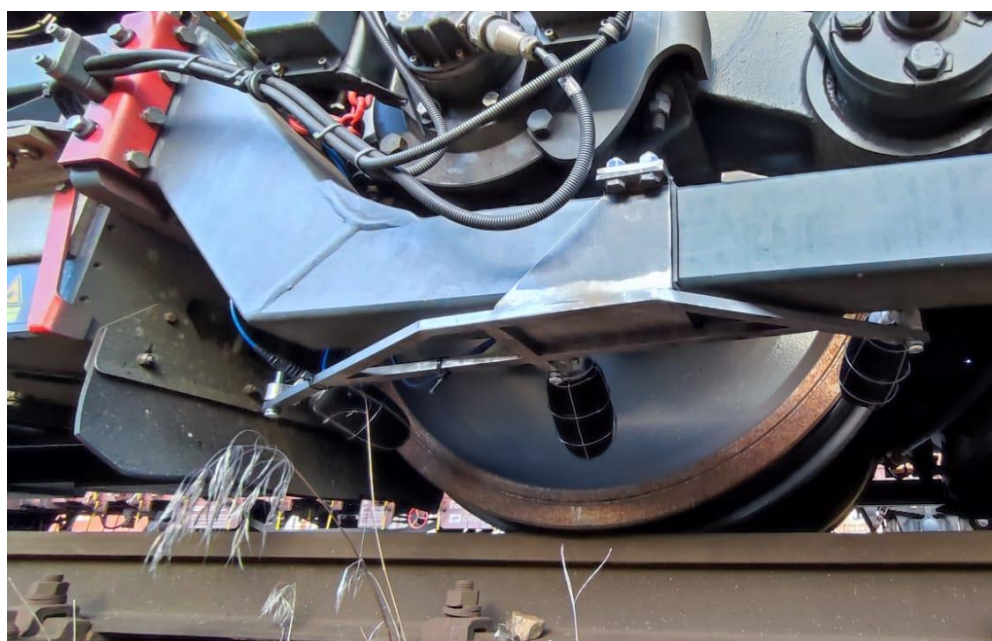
Prototypování neinvazivního kotevního přípravku vzorkem získaným 3D tiskem [zdroj: autoři]
